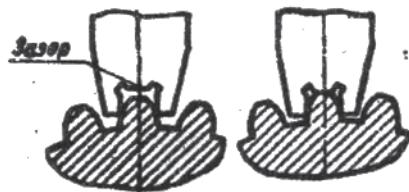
Схема замера зубчатого колеса с помощью пластинчатого шаблона
